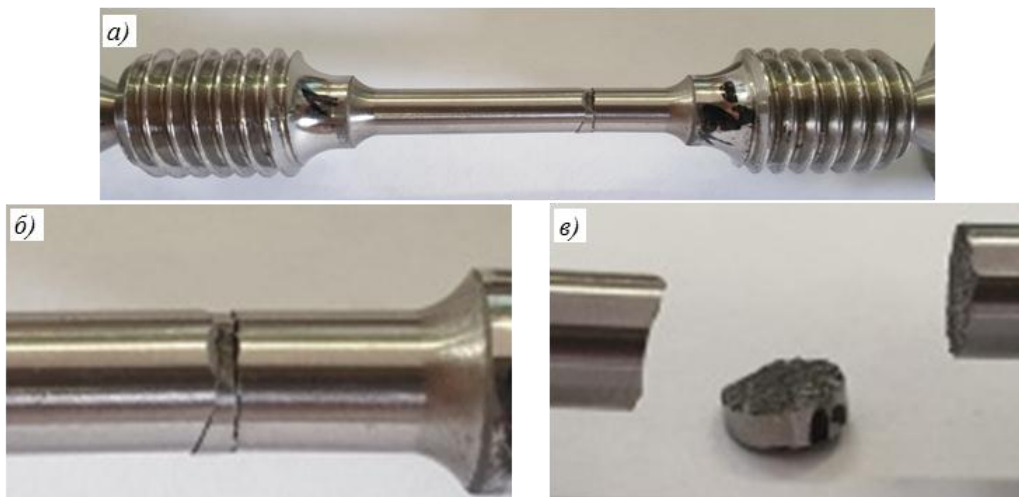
Общий вид образца 2 (а), область разрушения (б) и центральная пластина разрушения (в)
